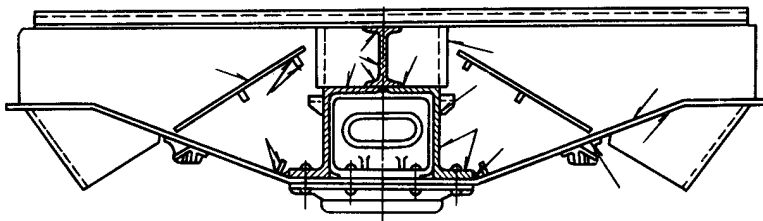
Сварные соединения шкворневого узла рамы полувагона
